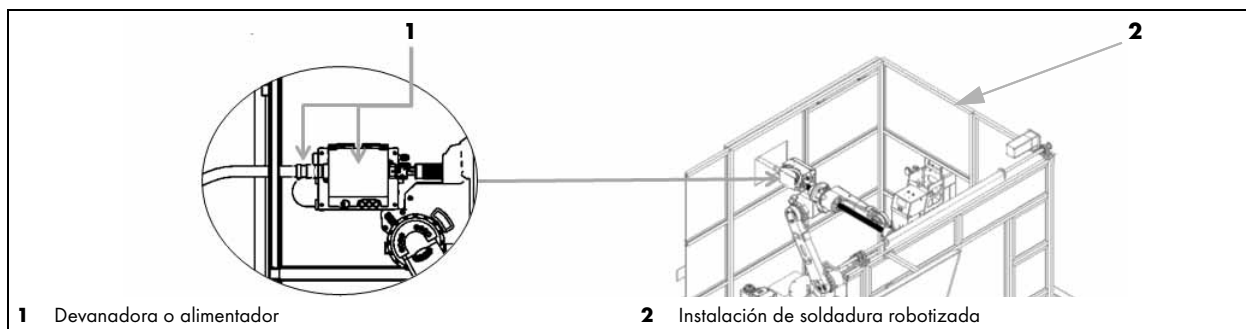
Montaje de la célula de soldadura robotizada
